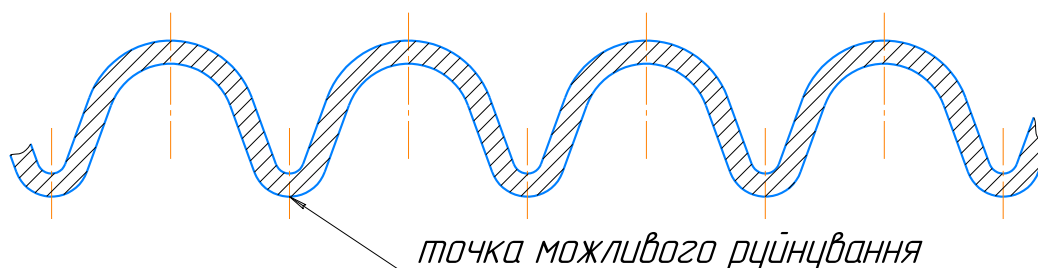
Гофрована листовая заготовка ножа бурякорізного
